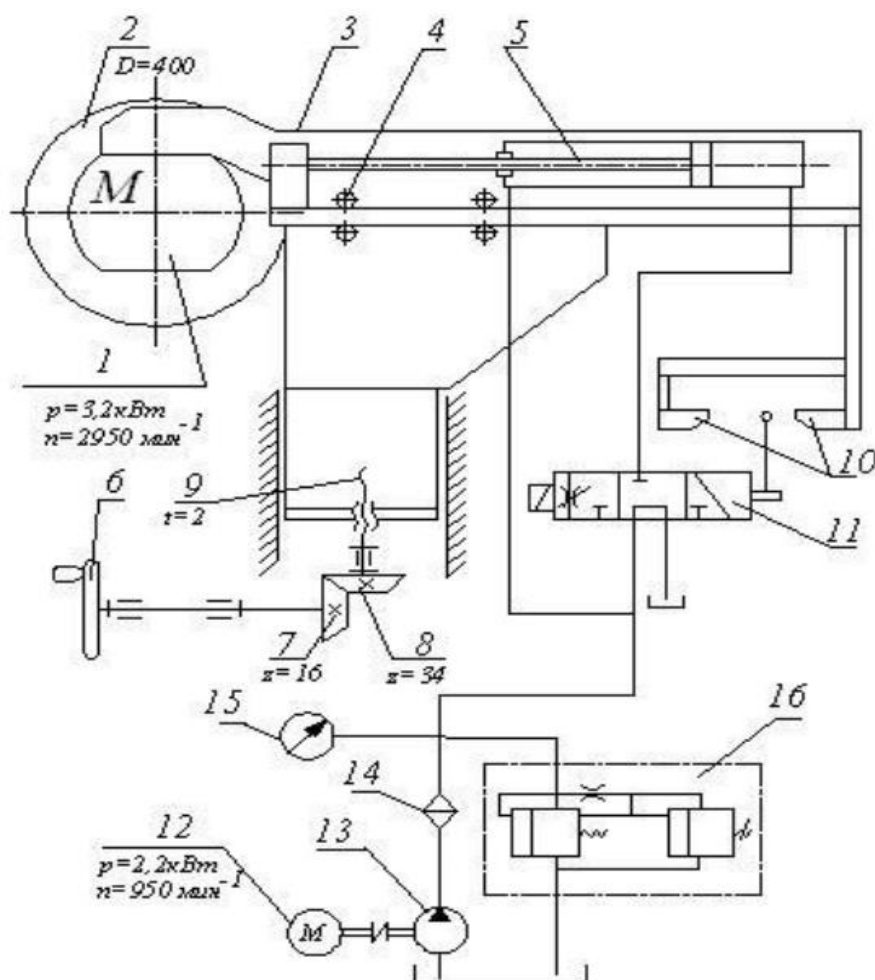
Гидрокинематическая схема торцовочного станка ЦПА40
